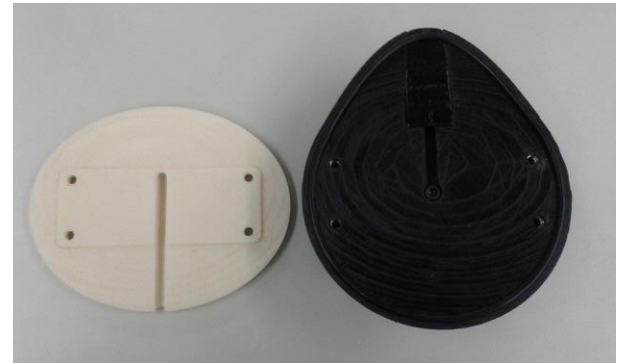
A la izquierda a parte superior del apoyo L3, a la derecha la parte inferior de la base de Soporte L3.
